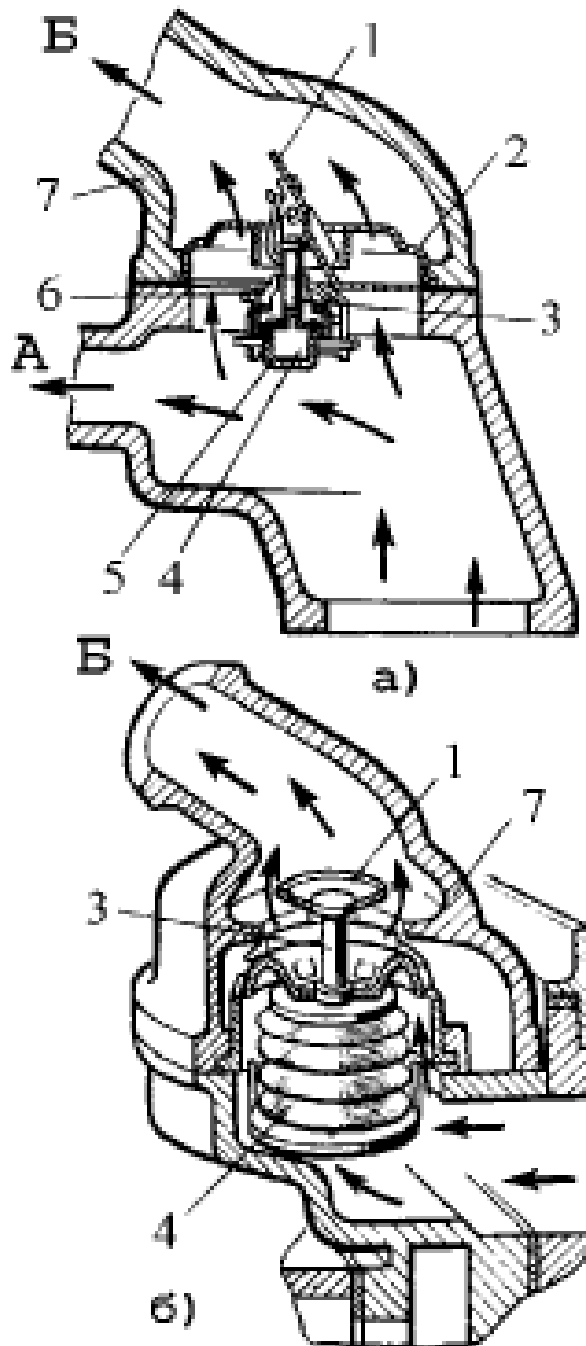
Схемы термостатов: а) с твердым наполнителем; б) с жидким наполнителем: 1 – клапан; 2 – корпус клапана; 3 – шток; 4 – наполнитель; 5 – баллон; 6 – возвратная пружина; 7 – корпус; А – направление потока жидкости в насос; Б – направление потока жидкости в радиатор
